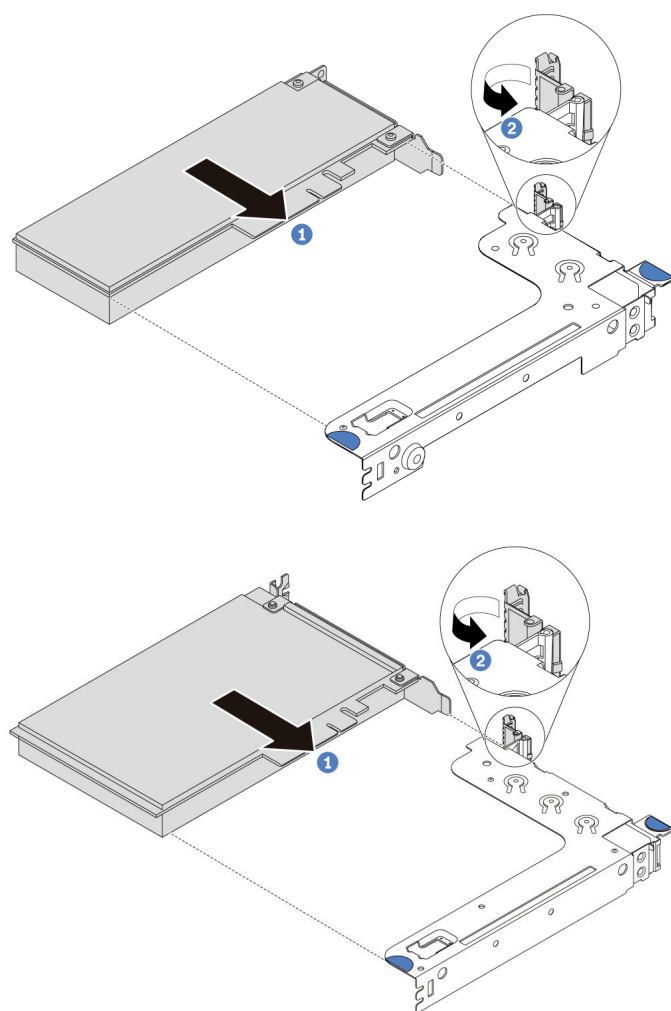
Installazione dell'assieme verticale 1 (LP/FHFL)
